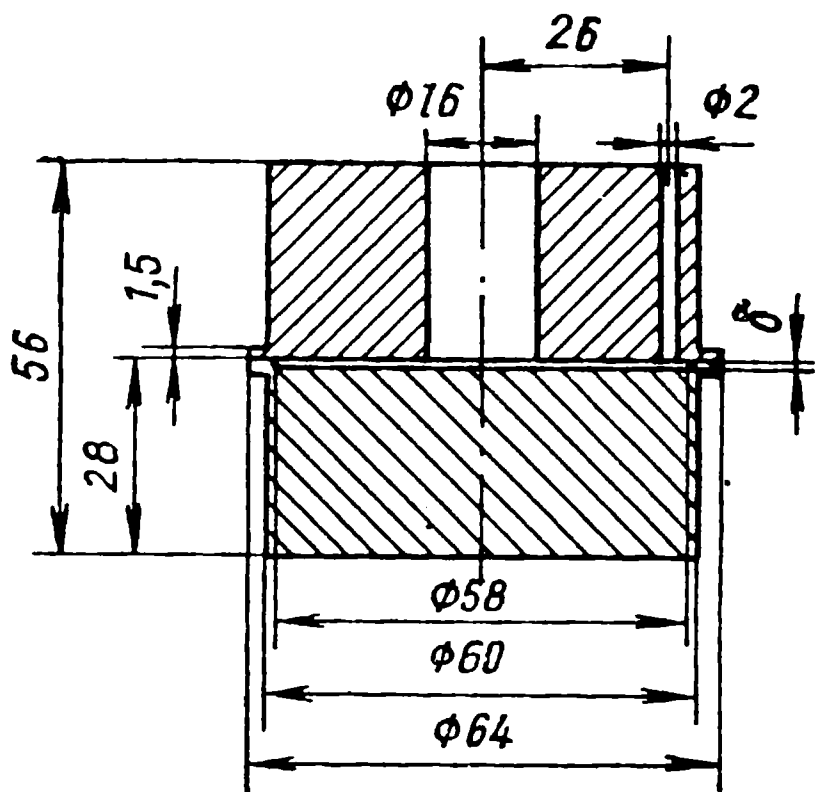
Заготовка под пайку для получения стыковых паяных образцов
